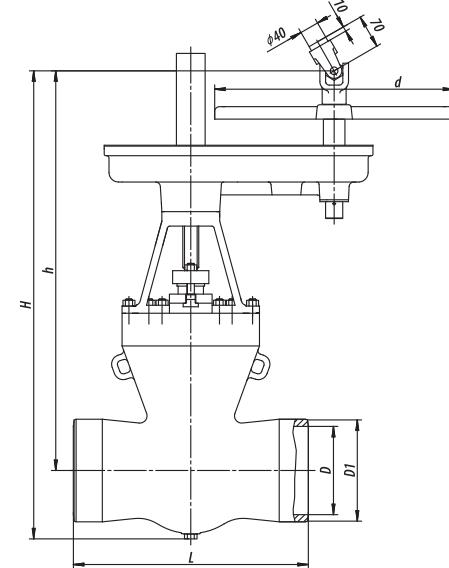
Задвижка DN150...400 с цилиндрическим редуктором
